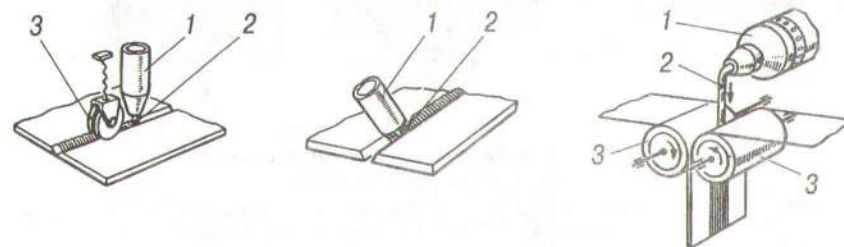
Схема зварювання термопластів екструдованою присадкою: 1 — екструдер; 2 — розплавлений матеріал; 3 — рамки
